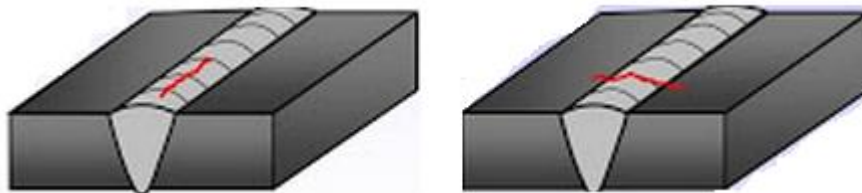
Fisuras longitudinales y transversales en soldadura
